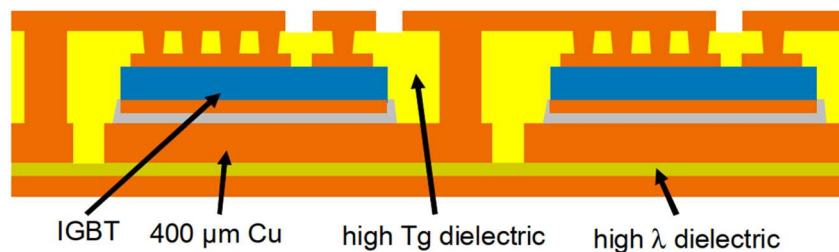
Enfouissement PCB avec frittage Ag en face arrière et microvias en face avant [136]
